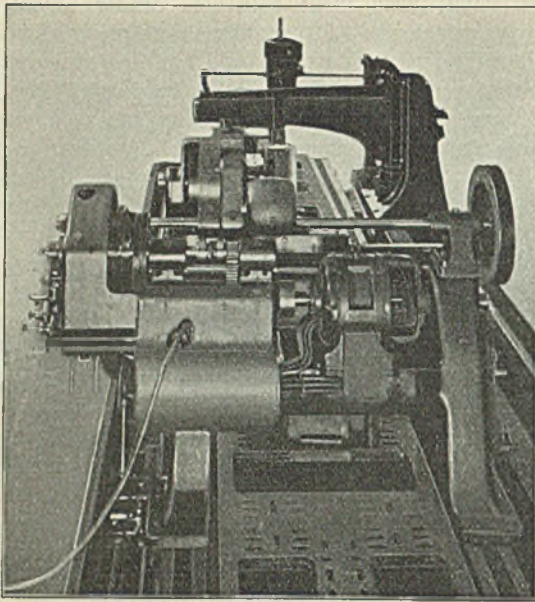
Platten-Hobel-, Stoß- und Bohrmaschine der Sächsischen Maschinen-Fabrik vorm. R. Hartmann in Chemnitz.
